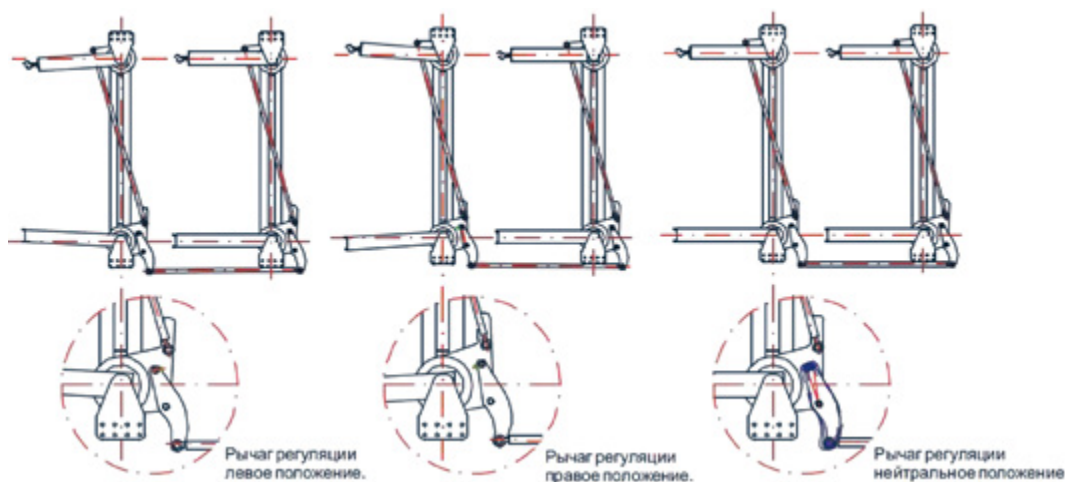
Внешний вид полюсов разъединителя во время регулировки
